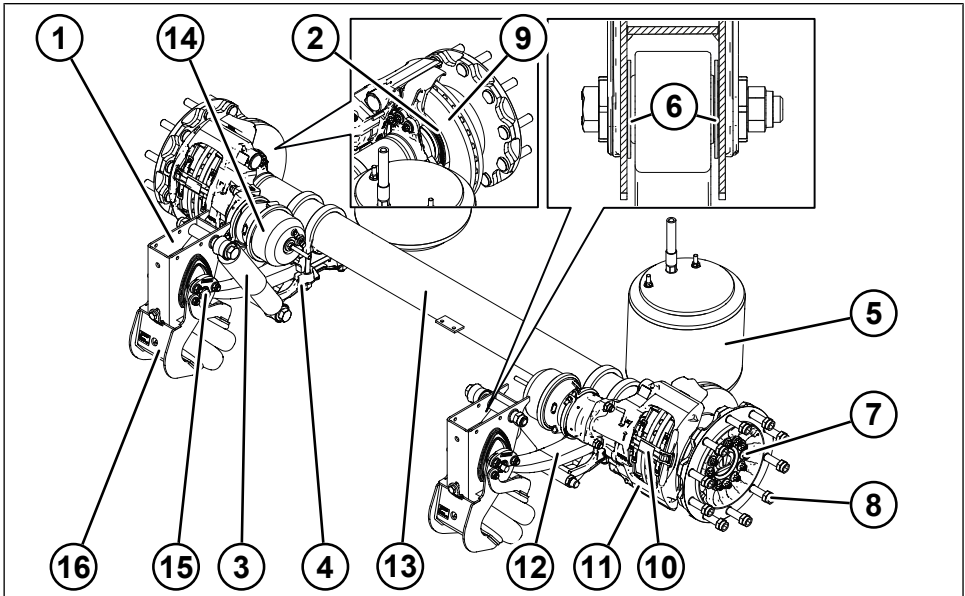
Vue d'ensemble de la maintenance (bras de suspension pneumatique inférieur)
